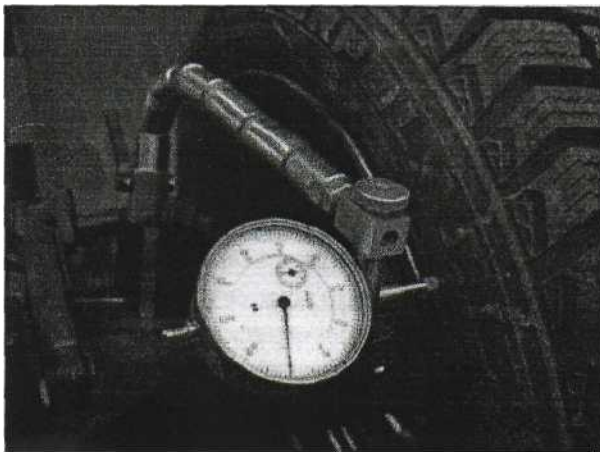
Установка индикатора для измерения бокового биения шины
